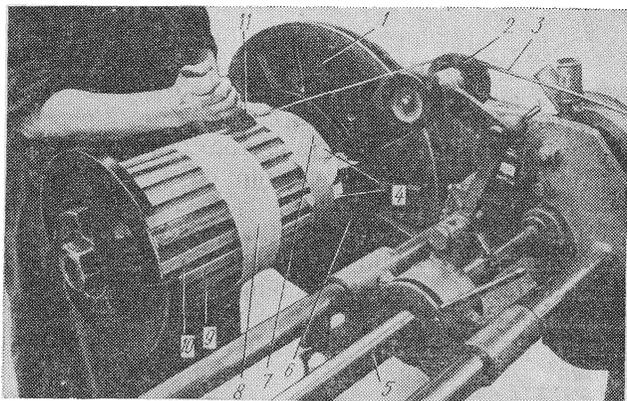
Намотка цилиндрической многослойной обмотки: 1 — планшайба намоточного станка, 2 — ролик раскладочного устройства, 3 — обмоточный провод, 4 — петли из хлопчатобумажной ленты, 5 — раскладочное устройство, 6 — гетинаксовый диск, 7 — разрезное бумажно-бакелитовое кольцо, 8 — хлопчатобумажная лента, временно закрепляющая рейки и планки, 9 — дистанционные рейки, 10 — технологические планки, 11 — клин (фибровый или деревянный)
